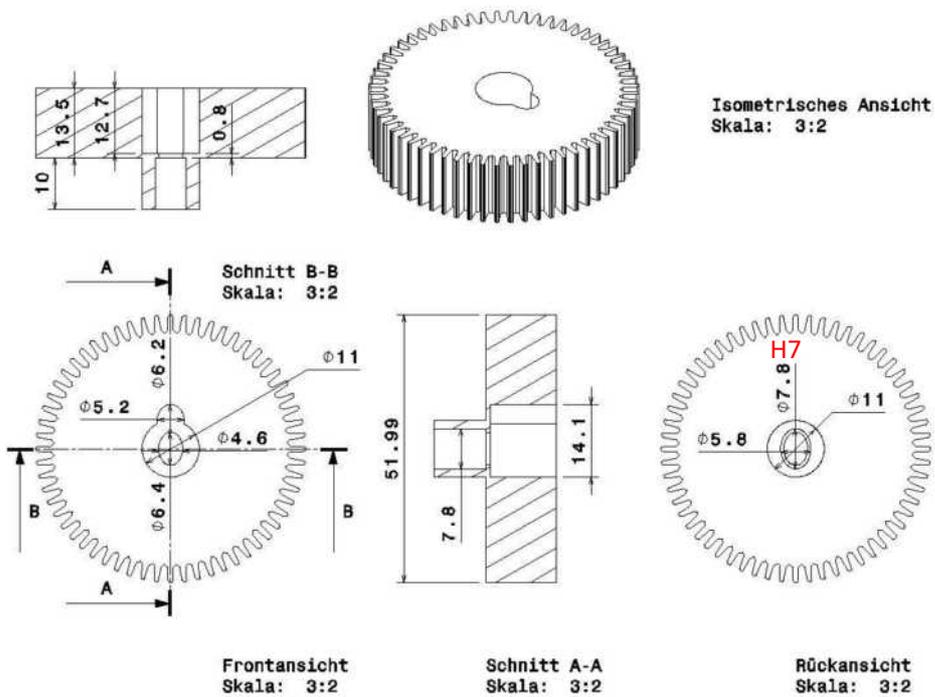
Element 20 (2D-Zeichnung) mit Toleranz
